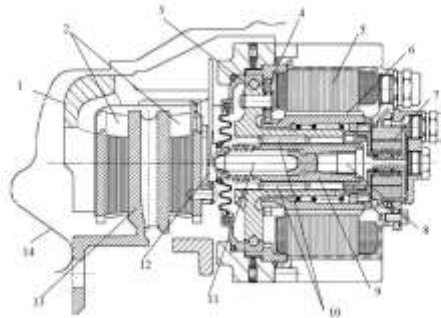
Конструкція виконавчого елемента; 1 – супорт; 2 – гальмівні колодки; 3 – центральний підшипник; 4 – планетарний механізм; 5 – статор; 6 – ротор/гайка; 7 – вирішальний пристрій; 8 – датчик сили; 9 – шпиндель; 10 – планетарні ролики; 11 – натискний шток; 12 – підтримка колодки; 13 – гальмівний диск; 14 – корпус.
